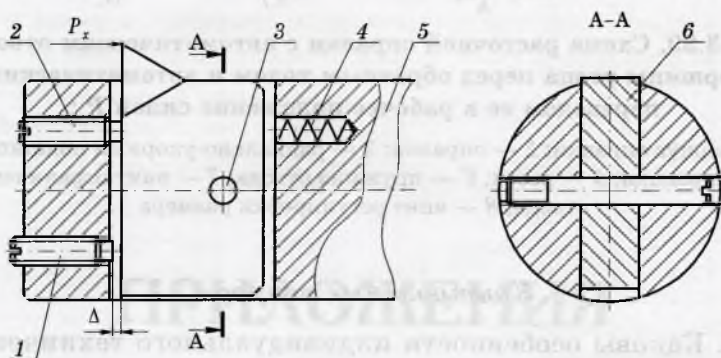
Схема управления положением вершины режущей кромки реза:
